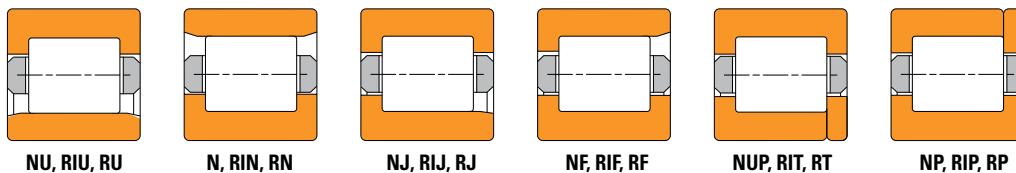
Bauarten metrischer/zölliger Standard-Zylinderrollenlager
